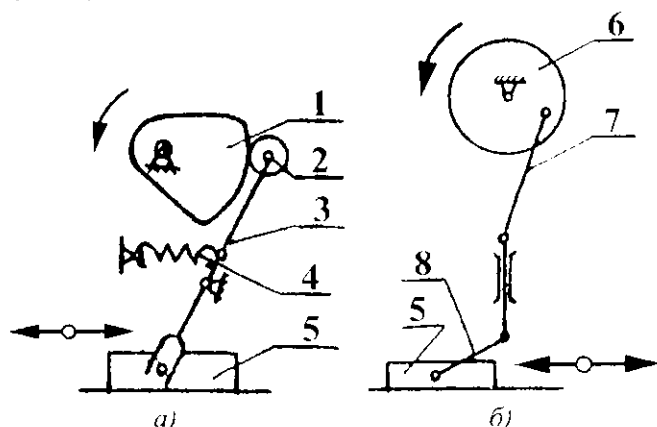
Схемы привода ползушки питателя от вала машины с помощью кулачка (а), эксцентрика (б): 1 – кулачок, 2 – ролик, 3 – рычаг, 4 – пружина, 5 – ползушка, 6 – диск, 7 – тяга, 8 – серьга
